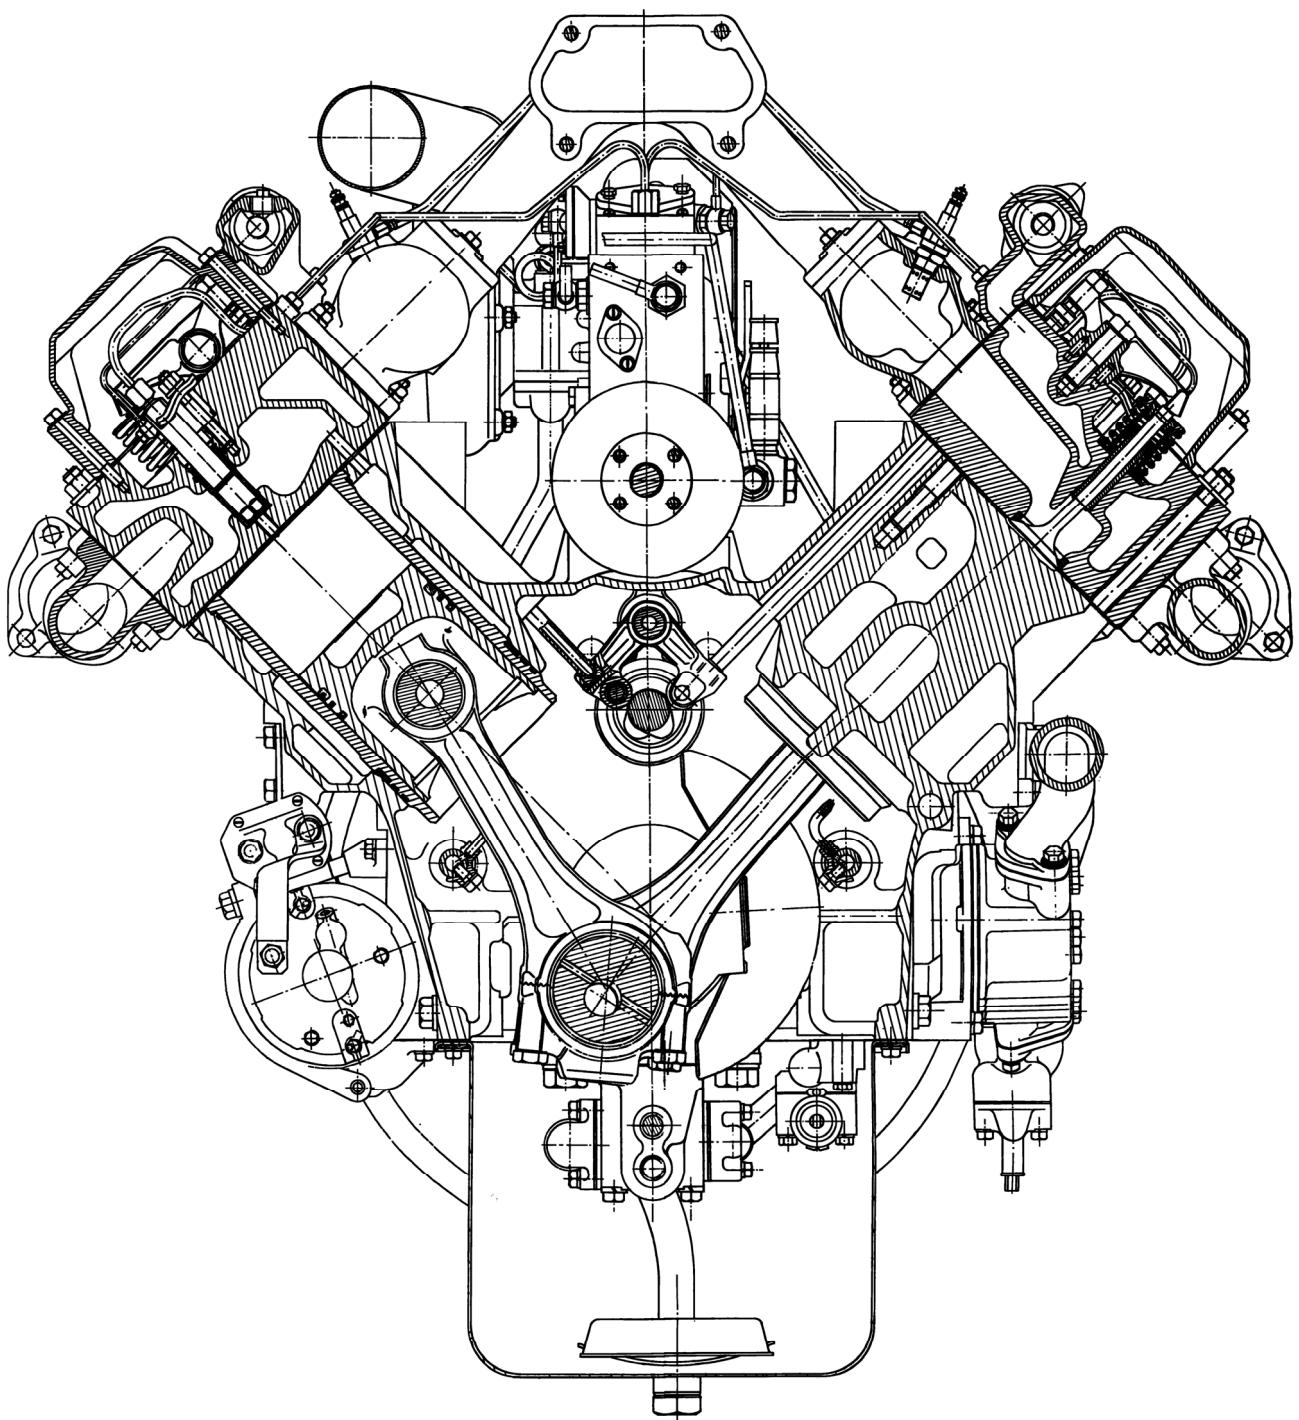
Поперечный разрез двигателя типа ЯМЗ-7511.10
